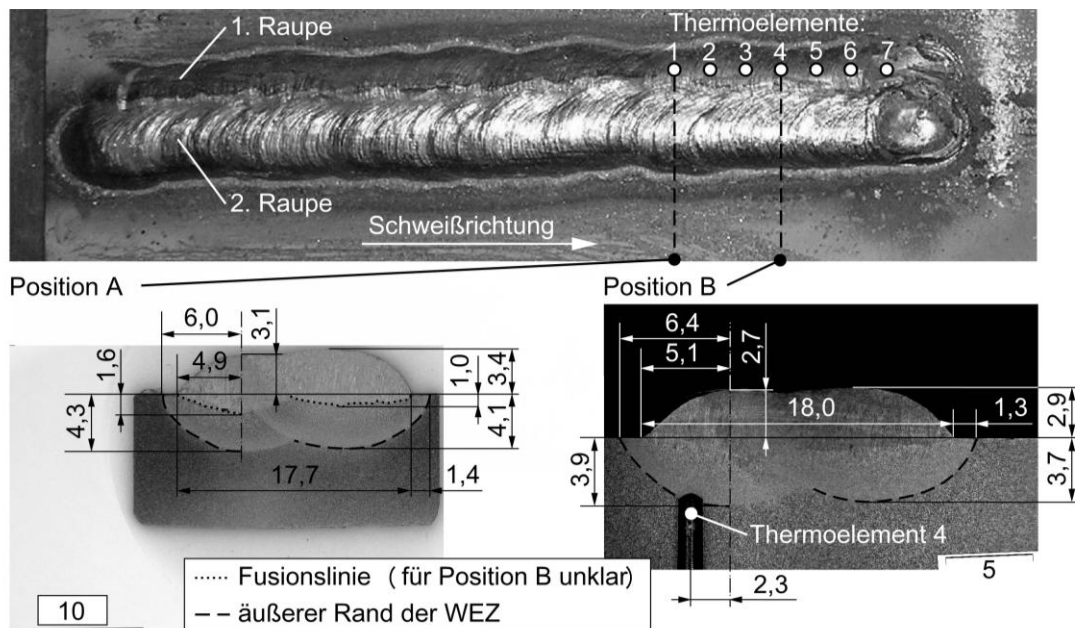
Makroschliffe für die Auftragsschweißung (Angaben in mm)
